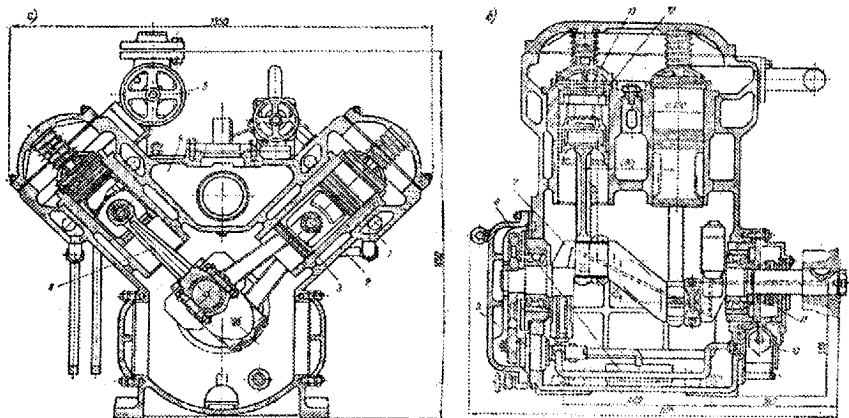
Чотирициліндровий компресор АУ-200: а – подовжній розріз; б – поперечний розріз; 1 – водяна рубашка; 2 – циліндрова гільза; 3 – поршень; 4 – шатун; 5 – нагнітальний вентиль; 6 – всмоктуюча порожнина; 7 – колінчастий вал; 8 – фільтр грубого очищення масла; 9 – шестерний насос; 10 – щілиний масляний фільтр; 11 – сальник; 12 – всмоктуючий клапан; 13 – нагнітальний клапан.
